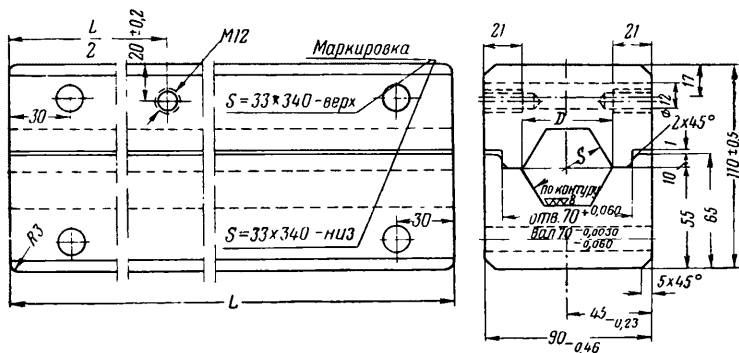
Пресс-форма для опрессовки и выпечки изоляции валов
